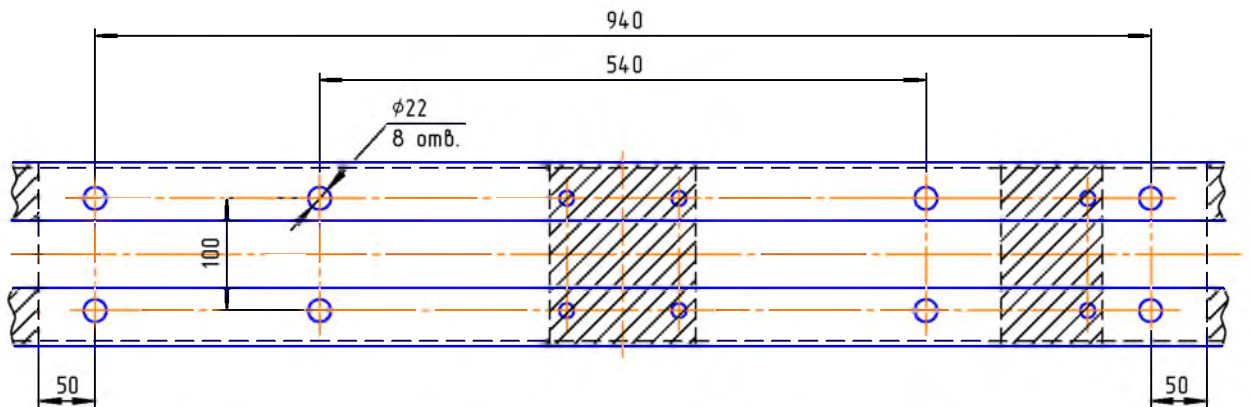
Присоединительные размеры для установки полюса на опорной конструкции
